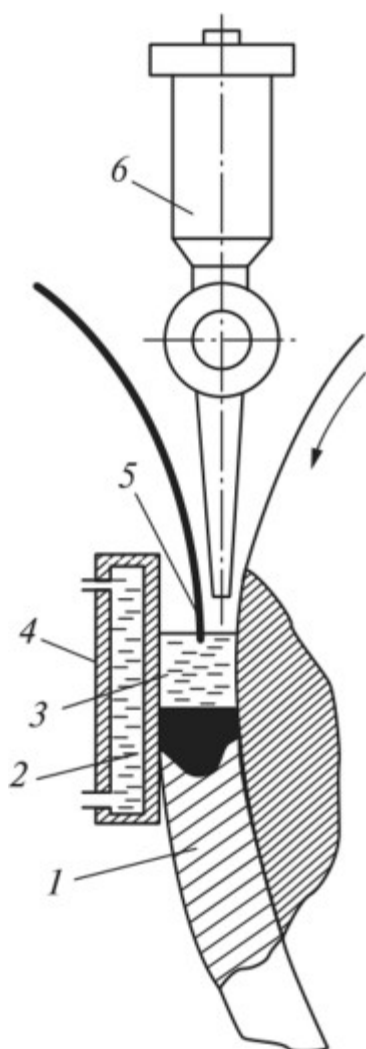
Схема ЭШН зернистым присадочным металлом:
